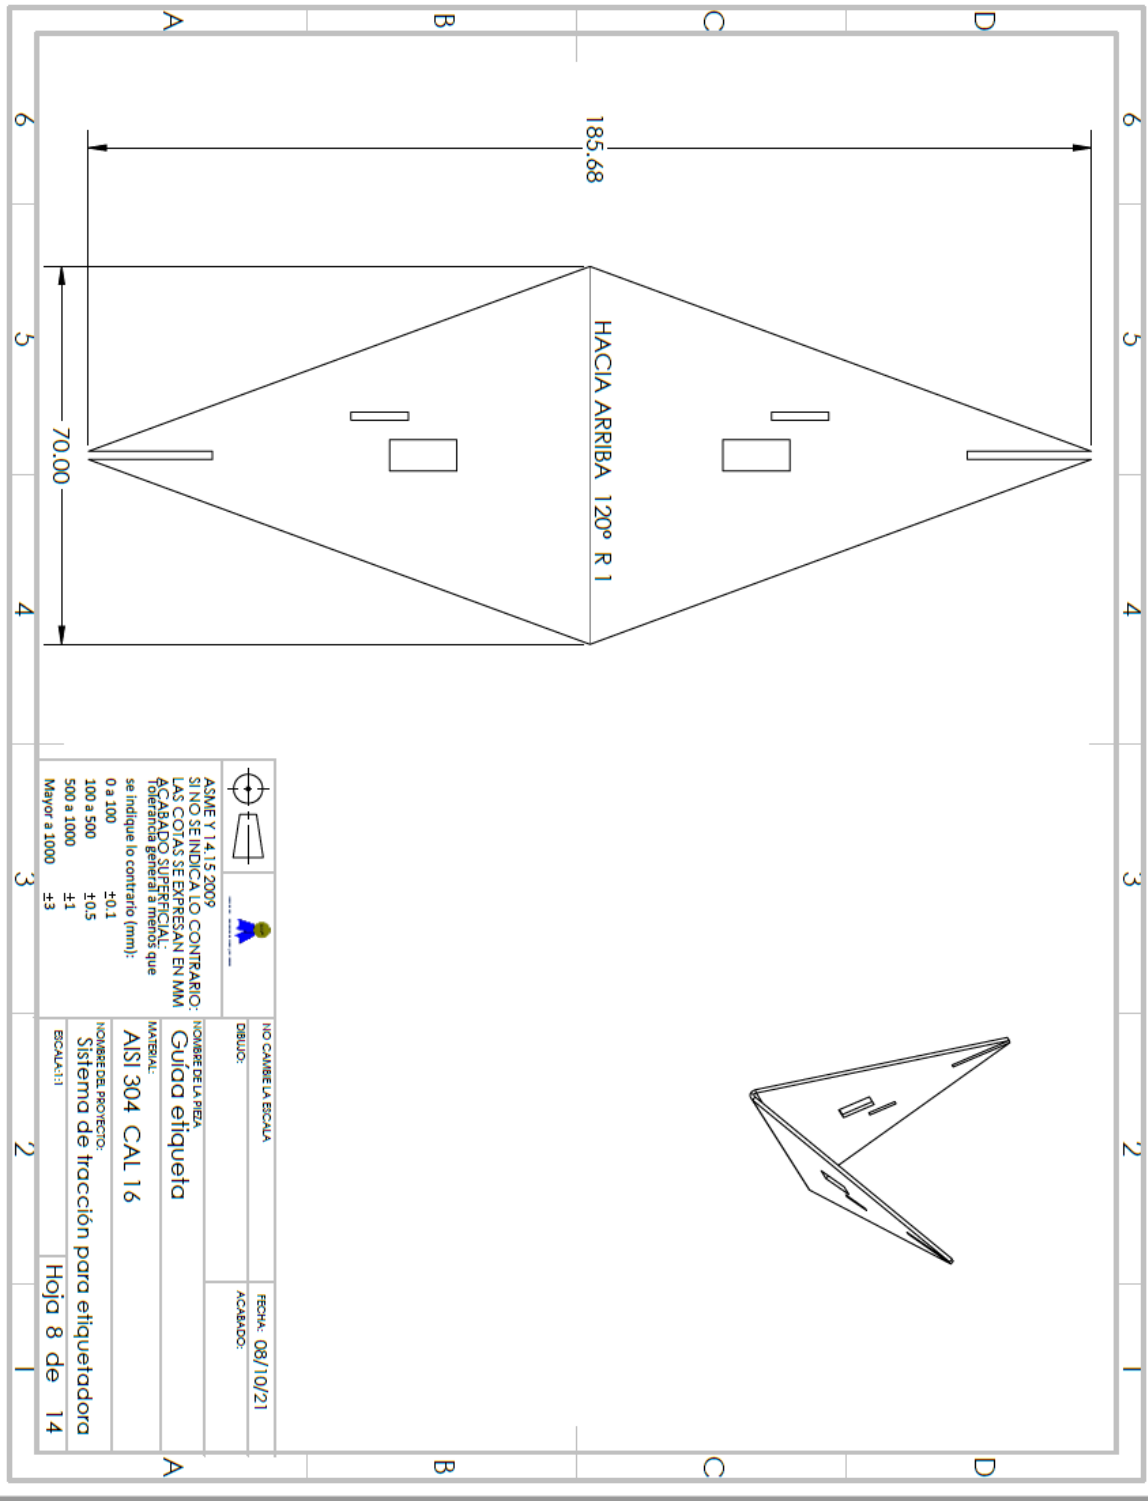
Plano auxiliar para el corte y dobléz del componente principal de la guía superior
